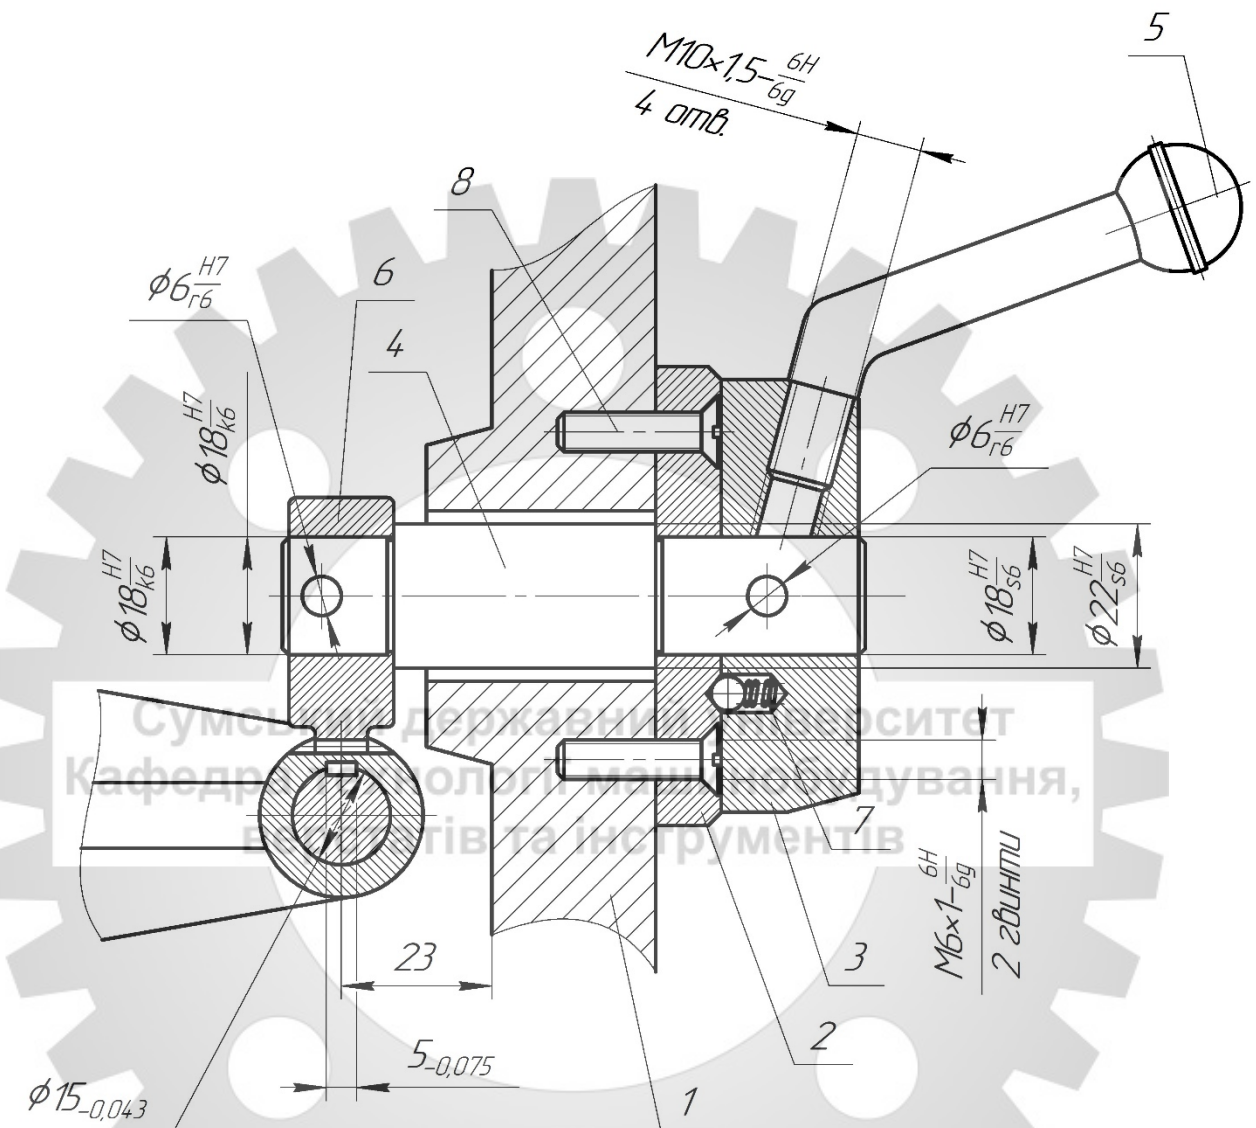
Конструкція перемикачів коробки швидкостей
